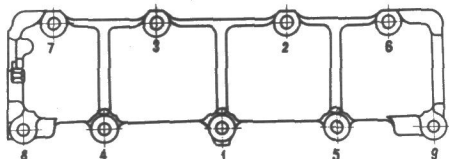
Порядок затягивания гаек крепления корпуса подшипников распределительного вала
